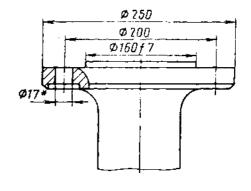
Эскиз присоединительной базы шпинделя $^{*}-$ 6 отверстий
